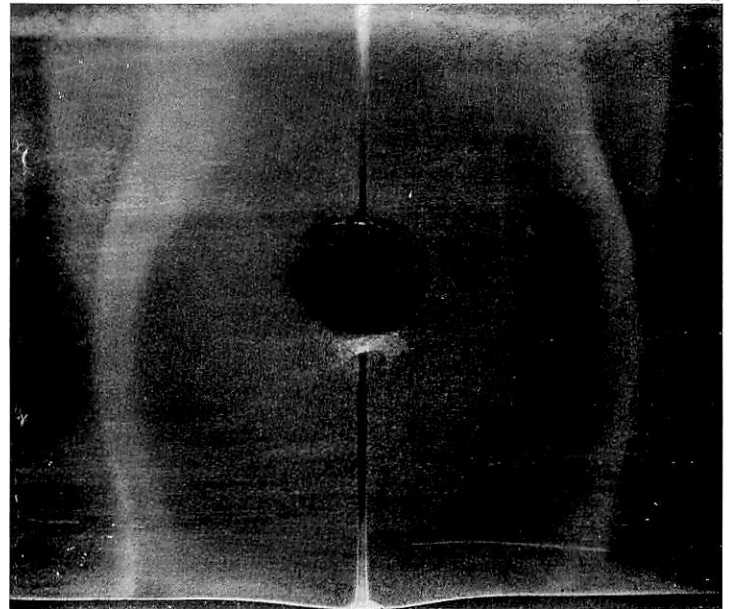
Thermit-Stumpfschweißung, geglüht. Ätzung II.
